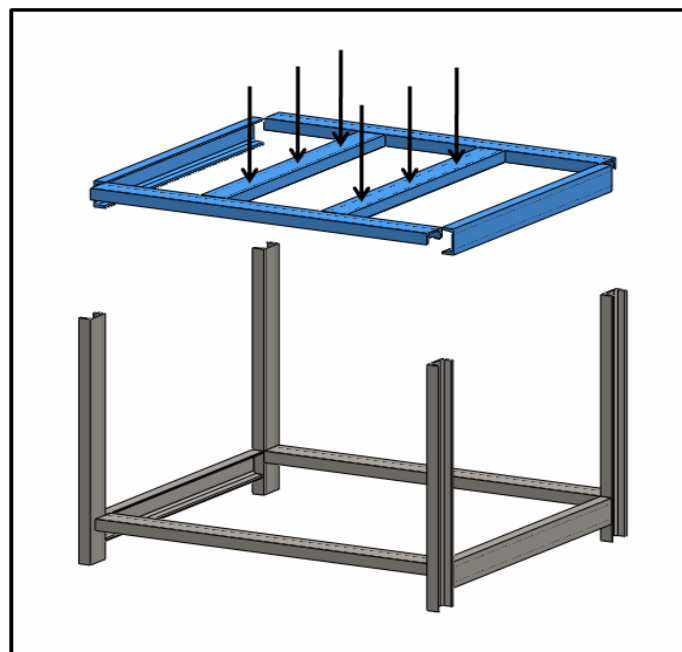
Vigas verticales de la estructura [Fuente: propio].
